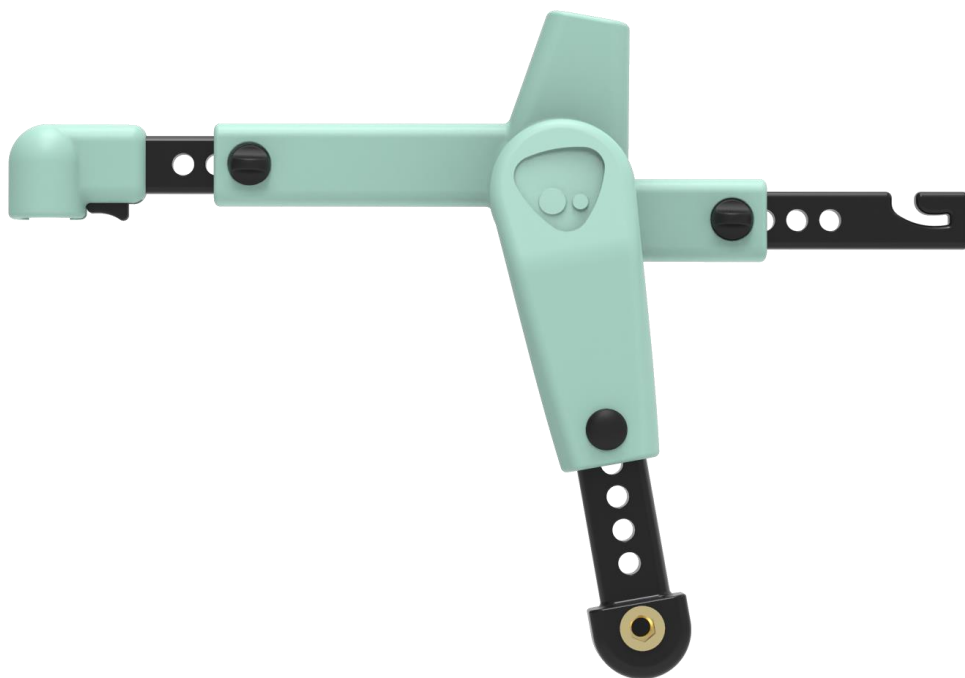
Tvarové řešení rámu – boční pohled.
